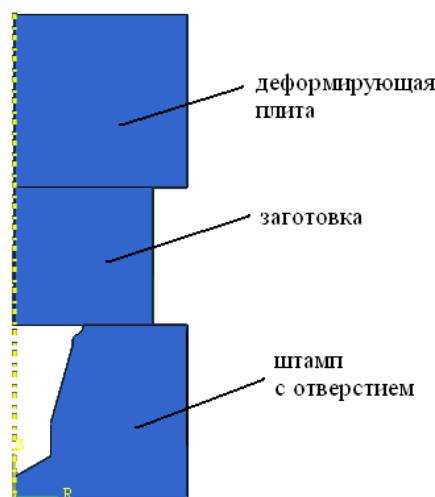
Сборка инструмента и заготовки в комплексе *Abaqus
